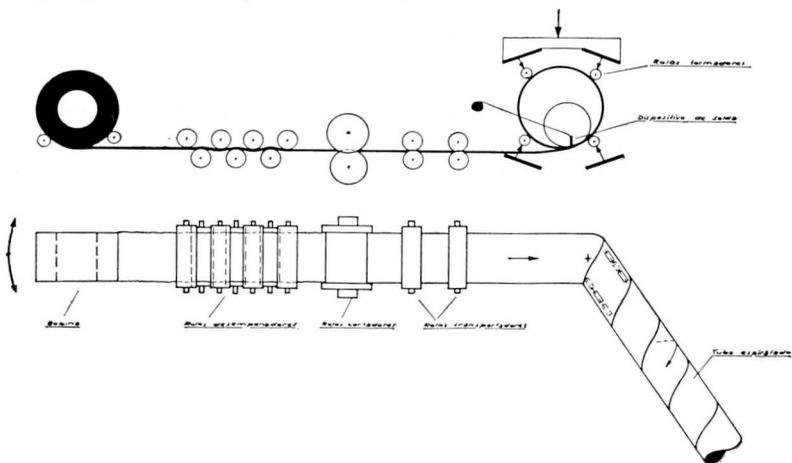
Esquema da máquina de soldar tubos espiralados. Dela há tipos transportáveis para o local das obras.
